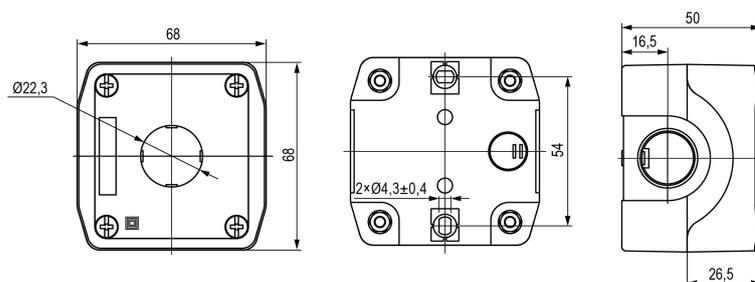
Габаритные и установочные размеры одноместного корпуса
